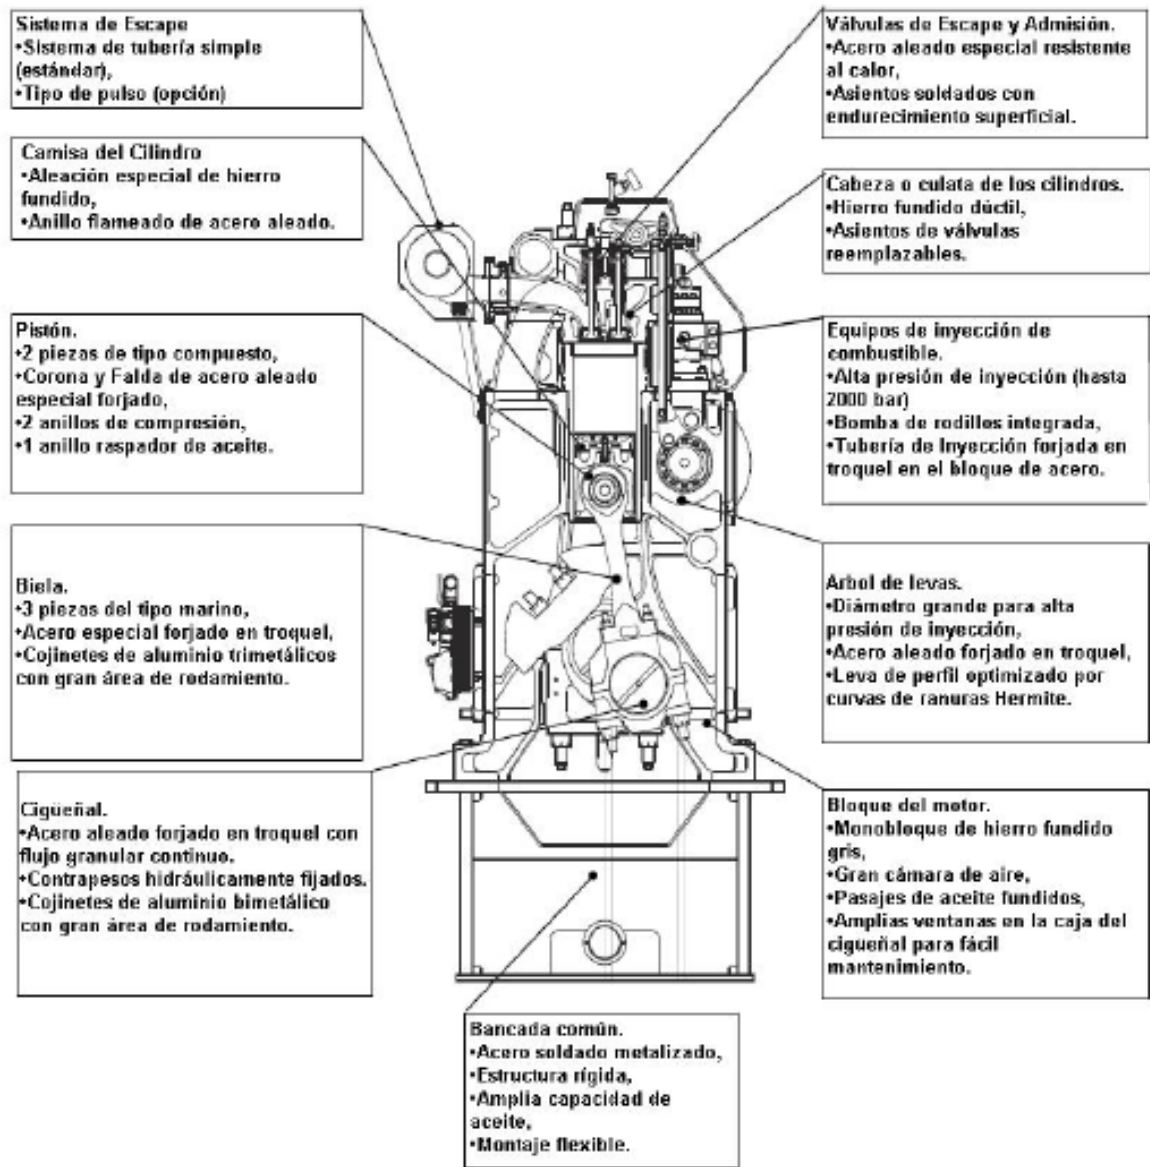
Partes fundamentales de los motores de combustión interna. Disposición física en el motor.
